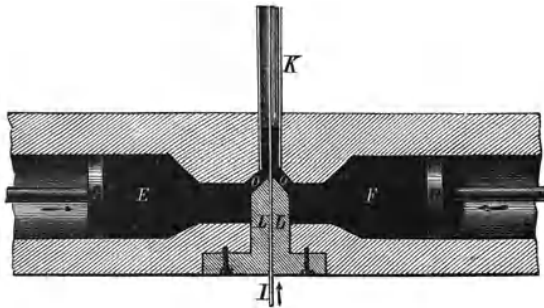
Prinzip der Guttaperchabedeckungsmaschine.
